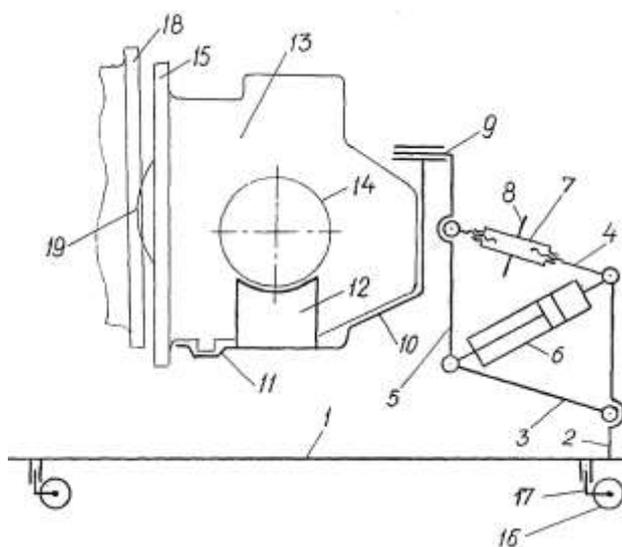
Схема подъемника для установки коробки перемены передач (патент № 2302991)
